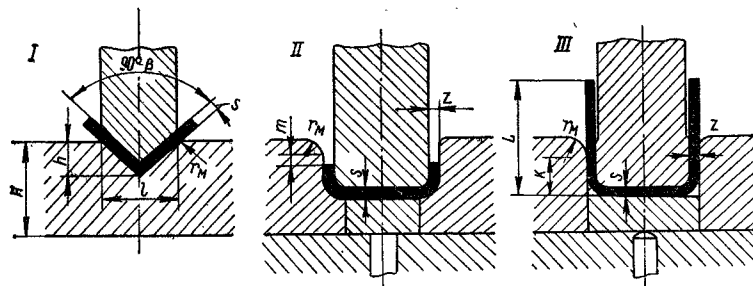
Конструктивные размеры гибочных штампов: I — для угловой гибки; II — для гибки скобы с короткими полками; III — для гибки скоб с длинными полками
